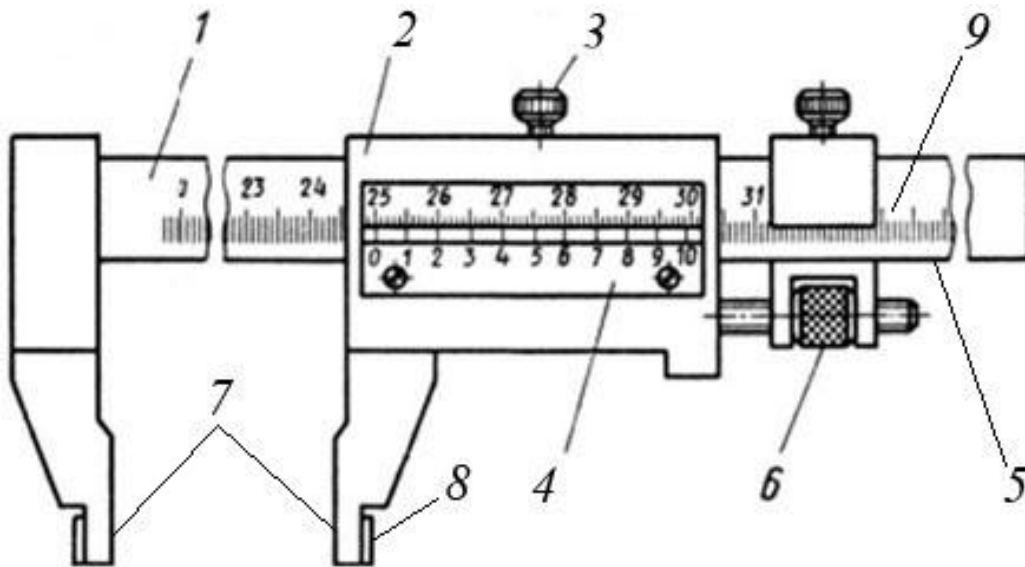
Конструкція та будова штангенциркуля ШЦ-III: 1 – штанга; 2 – рамка; 3 – фіксатор; 4 – ноніус; 5 – робоча поверхня штанги; 6 – пристрій тонкої установки рамки; 7 – губки з плоскими вимірними поверхнями для вимірювання зовнішніх розмірів; 8 – губки з циліндровими вимірними поверхнями для вимірювання внутрішніх розмірів; 9 – шкала штанги
